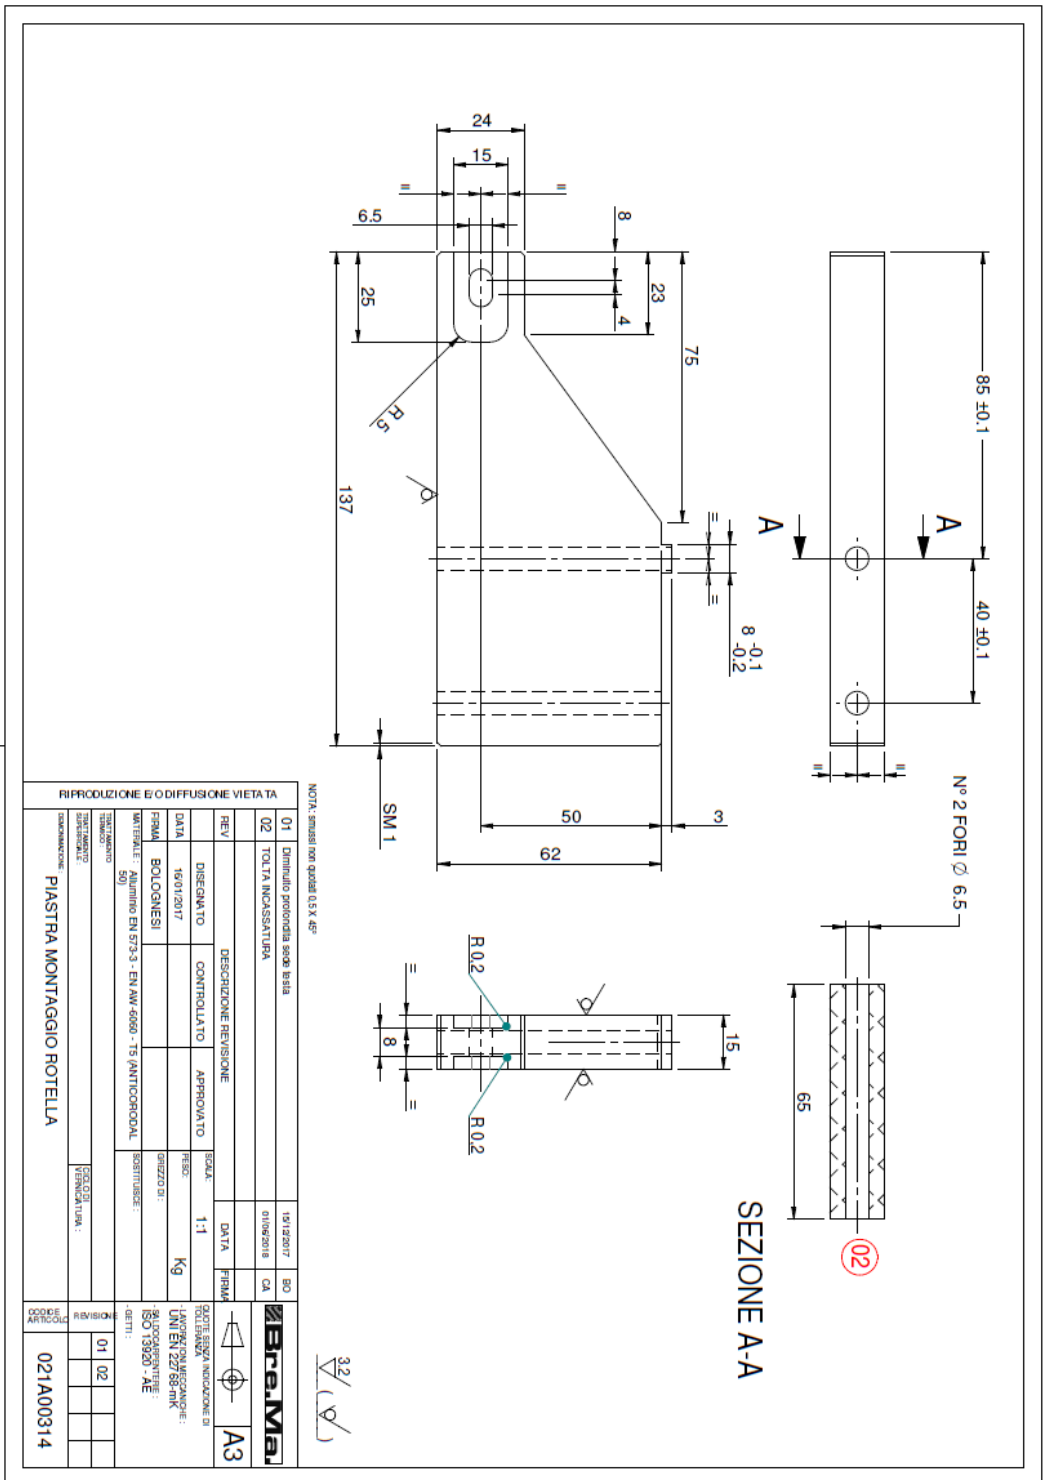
Disegno tecnico PIASTRA MONTAGGIO ROTELLA
